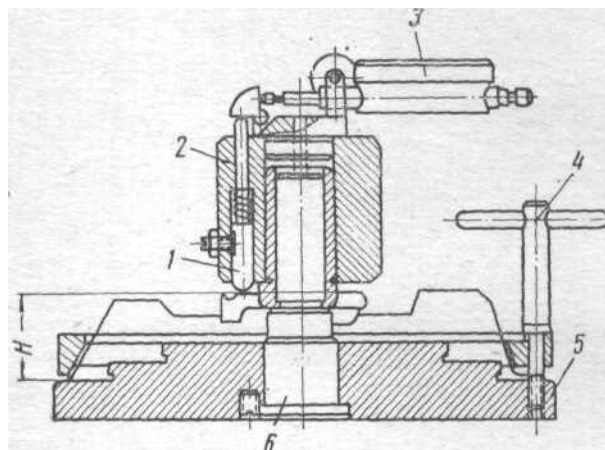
Приспособление для проверки биения пяты рычагов выключения сцепления:
